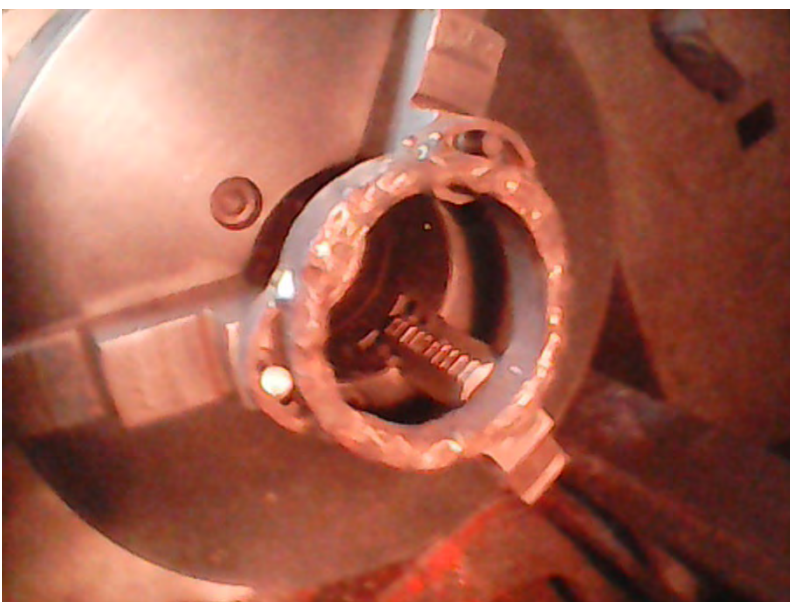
Внешний вид приспособления для расточки прямых кулачков
